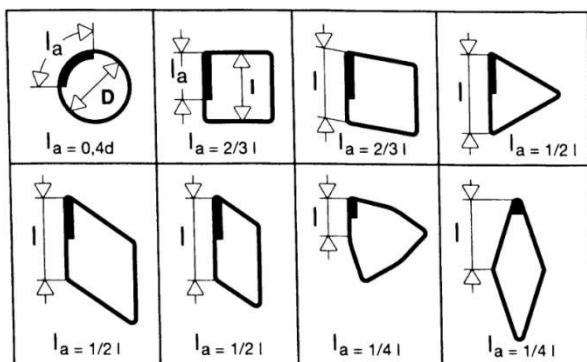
Форма поверхности и эффективная длина режущей пластины
